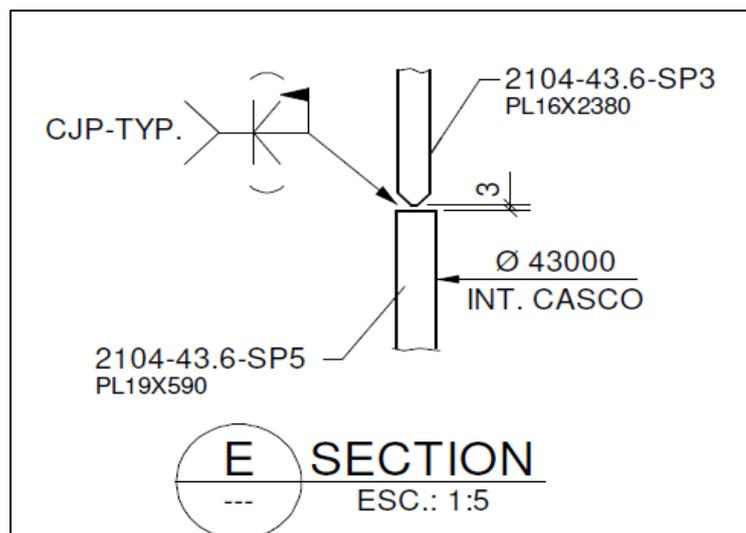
Detalle de soldadura entre Anillos de casco
